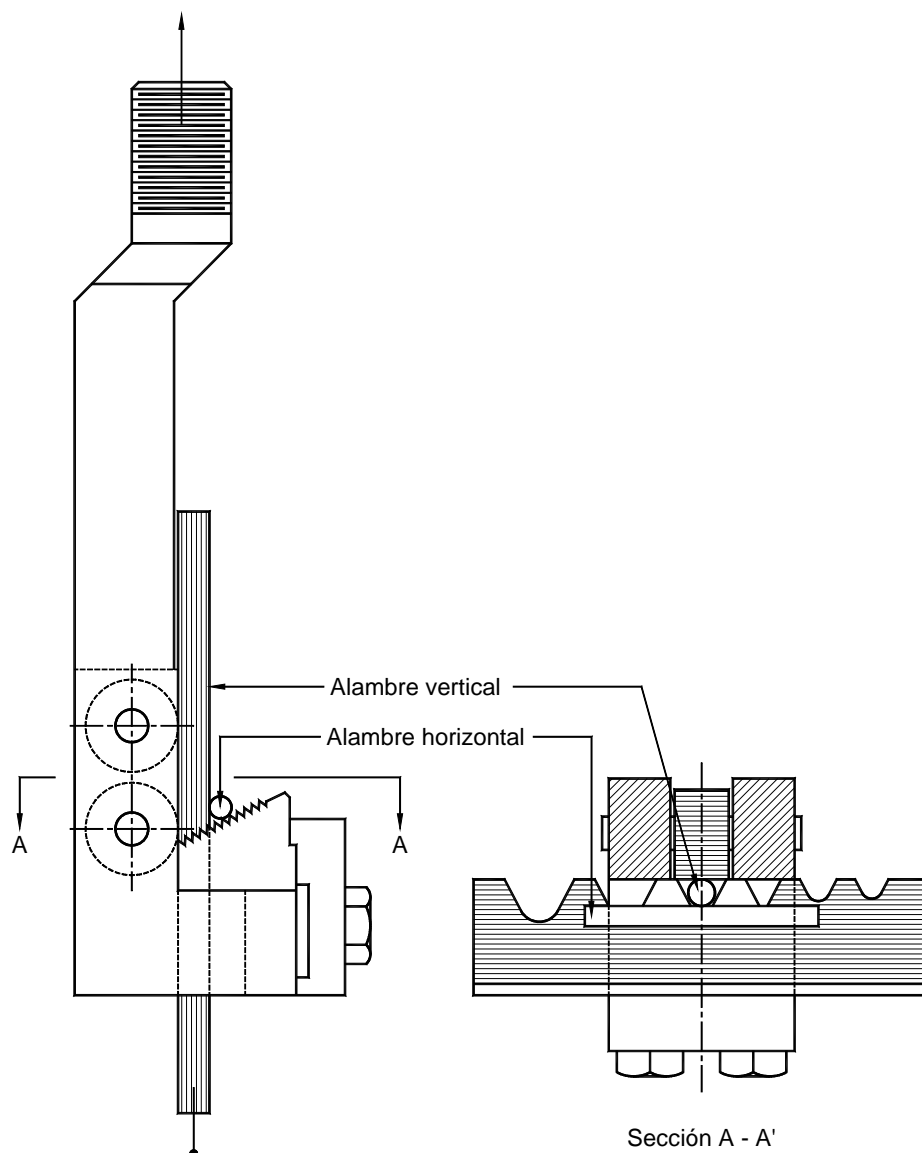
Dispositivo de ensayo para la soldadura de malla electrosoldada
